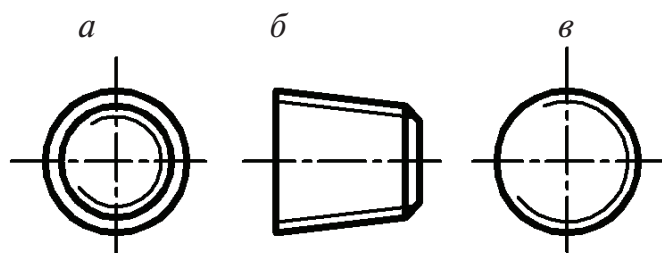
Пример изображения на чертеже наружной конической резьбы (на стержне):
